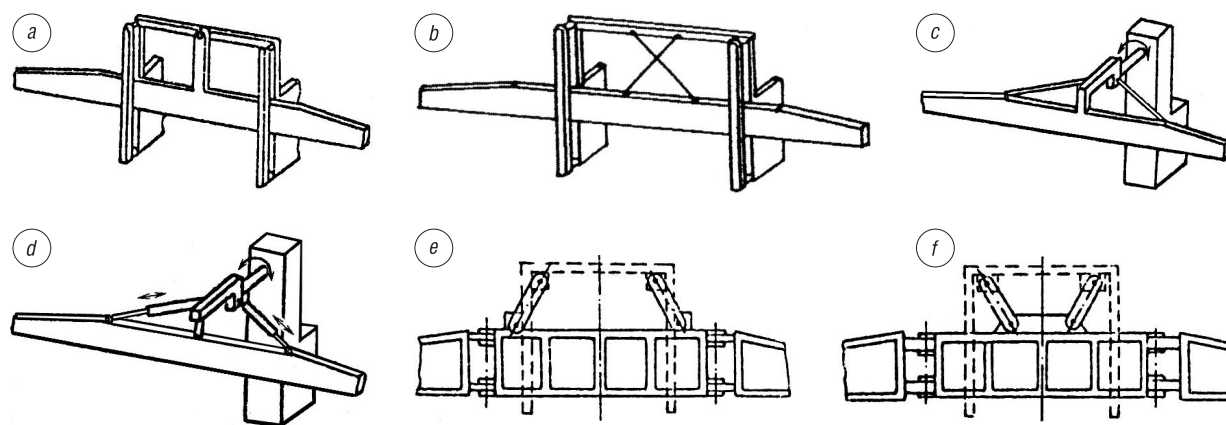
Схемы подвесок несущих конструкций штанг к раме опрыскивателя: *a* – ведомый направленный маятник; *b* – направленный канатный маятник; *c* – жесткий маятник; *d* – свободный маятник; *e* – двухшарнирная А-образной формы; *f* – двухшарнирная V-образной формы
